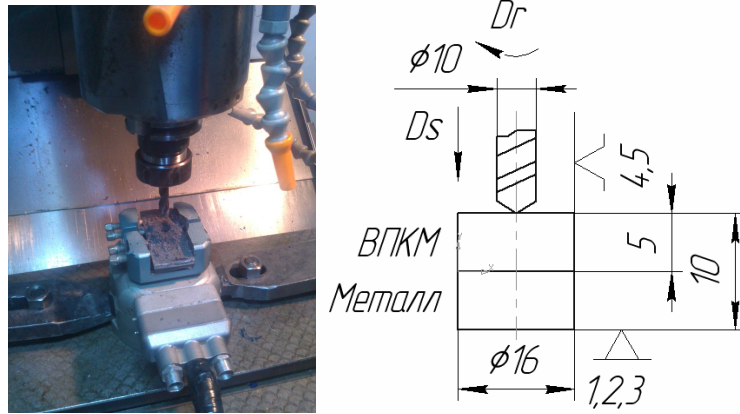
Сверление отверстий на фрезерном станке
